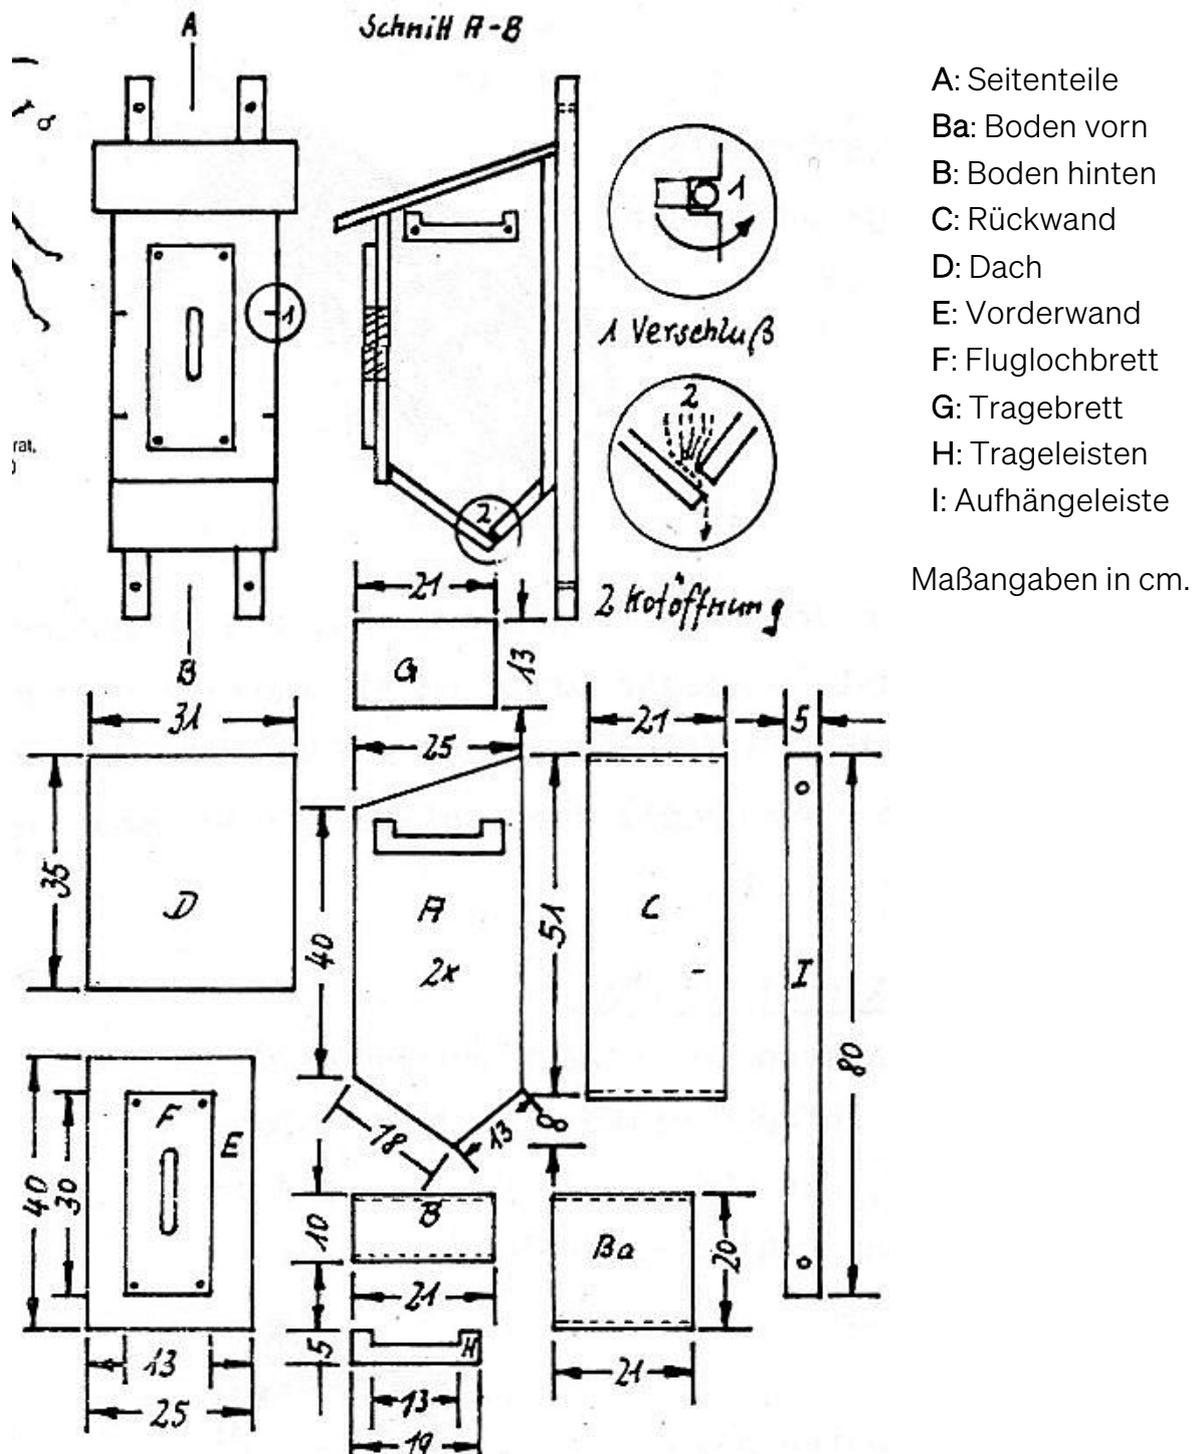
Bauplan für einen Hornissenkasten, Quelle: NABU Rinteln.
